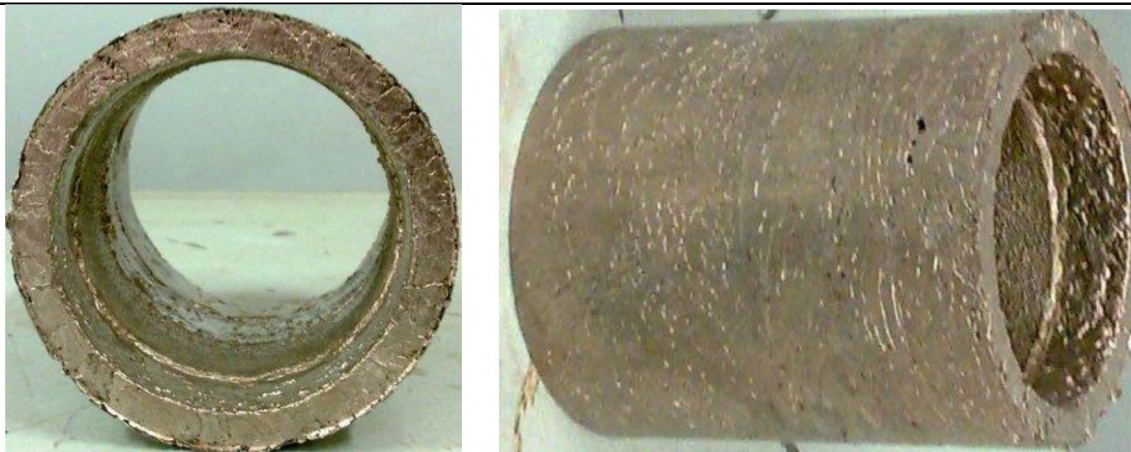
Отливка, полученная на лабораторной установке центробежного литья.
